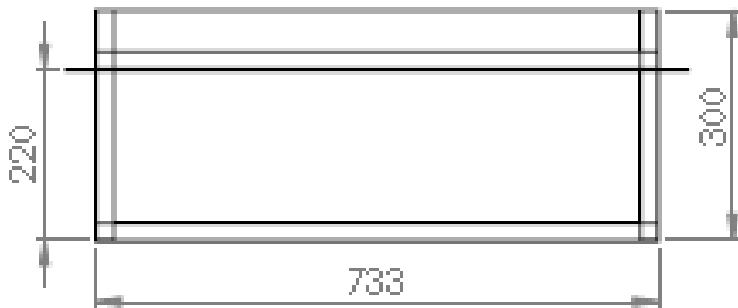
Vista lateral da caixa do banco de baterias traseiro
